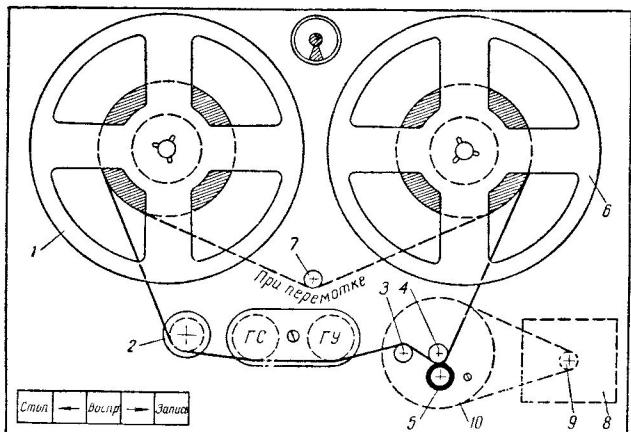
Лентопротяжный механизм: 1 — левая подающая кассета, 2, 3 — направляющие ролики, 4 — ведущий вал, 5 — прижимной ролик, 6 — правая принимающая кассета, 7 — направляющая колонка, 8 — ведущий двигатель, 9 — шкив ведущего двигателя, 10 — маховик.
